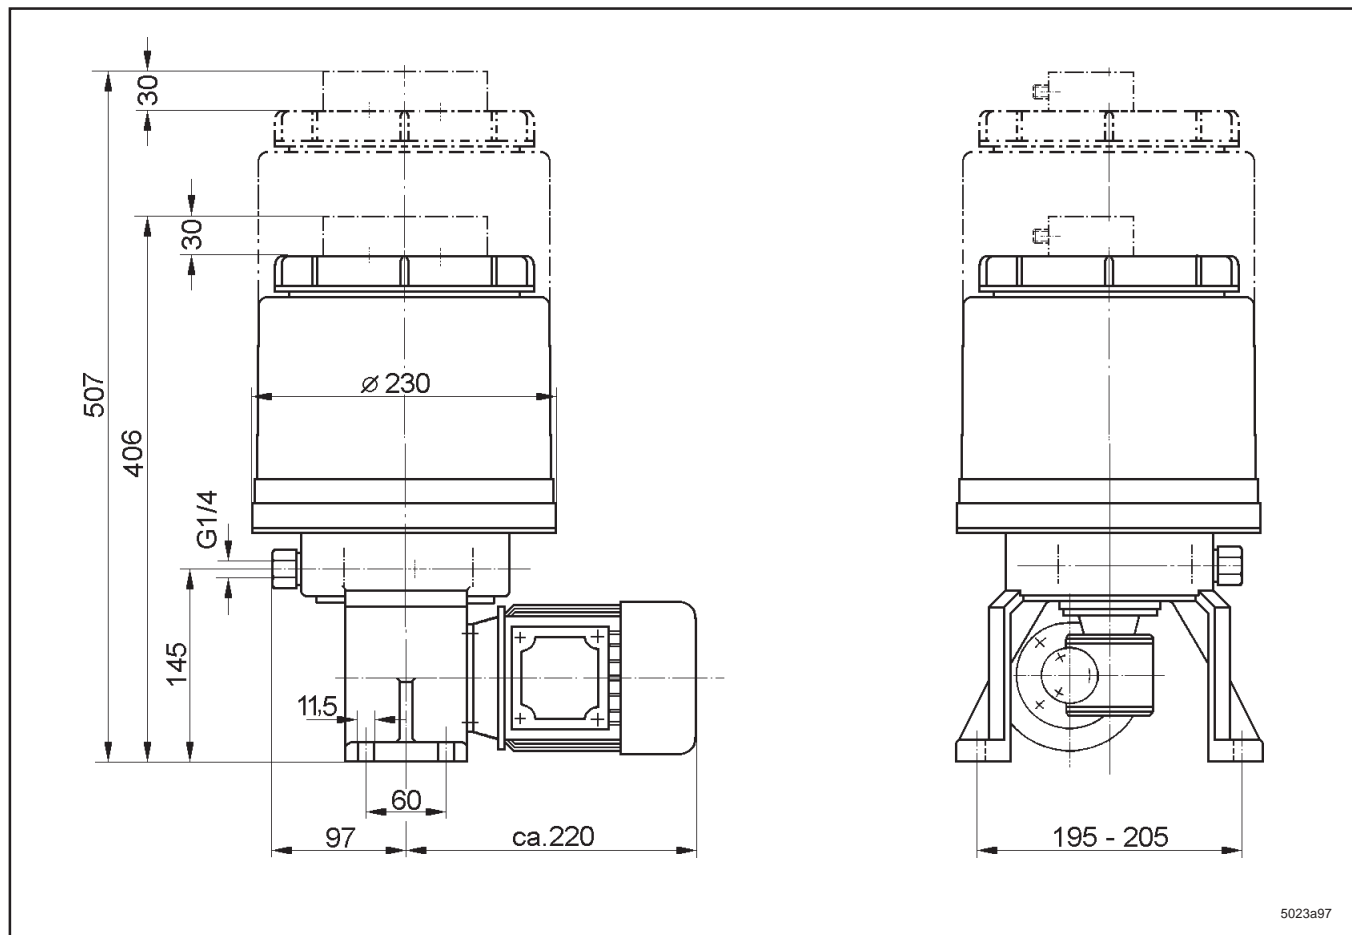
Maßzeichnung für Pumpe P 205, 1-stufiges Getriebe, 4/8l Kunststoffbehälter, Motorantrieb
